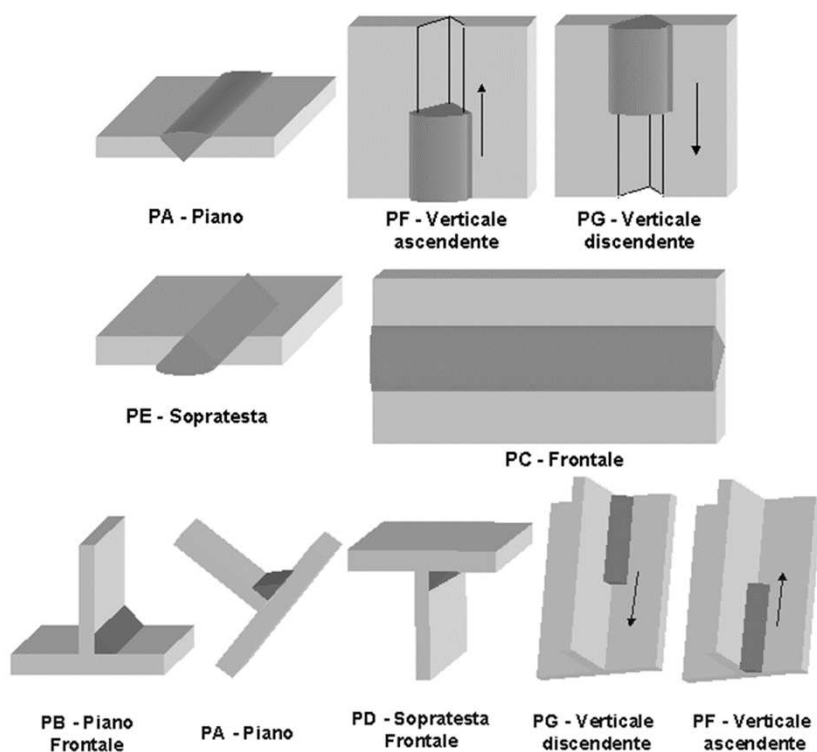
Posições de soldadura. Fonte: IIS
